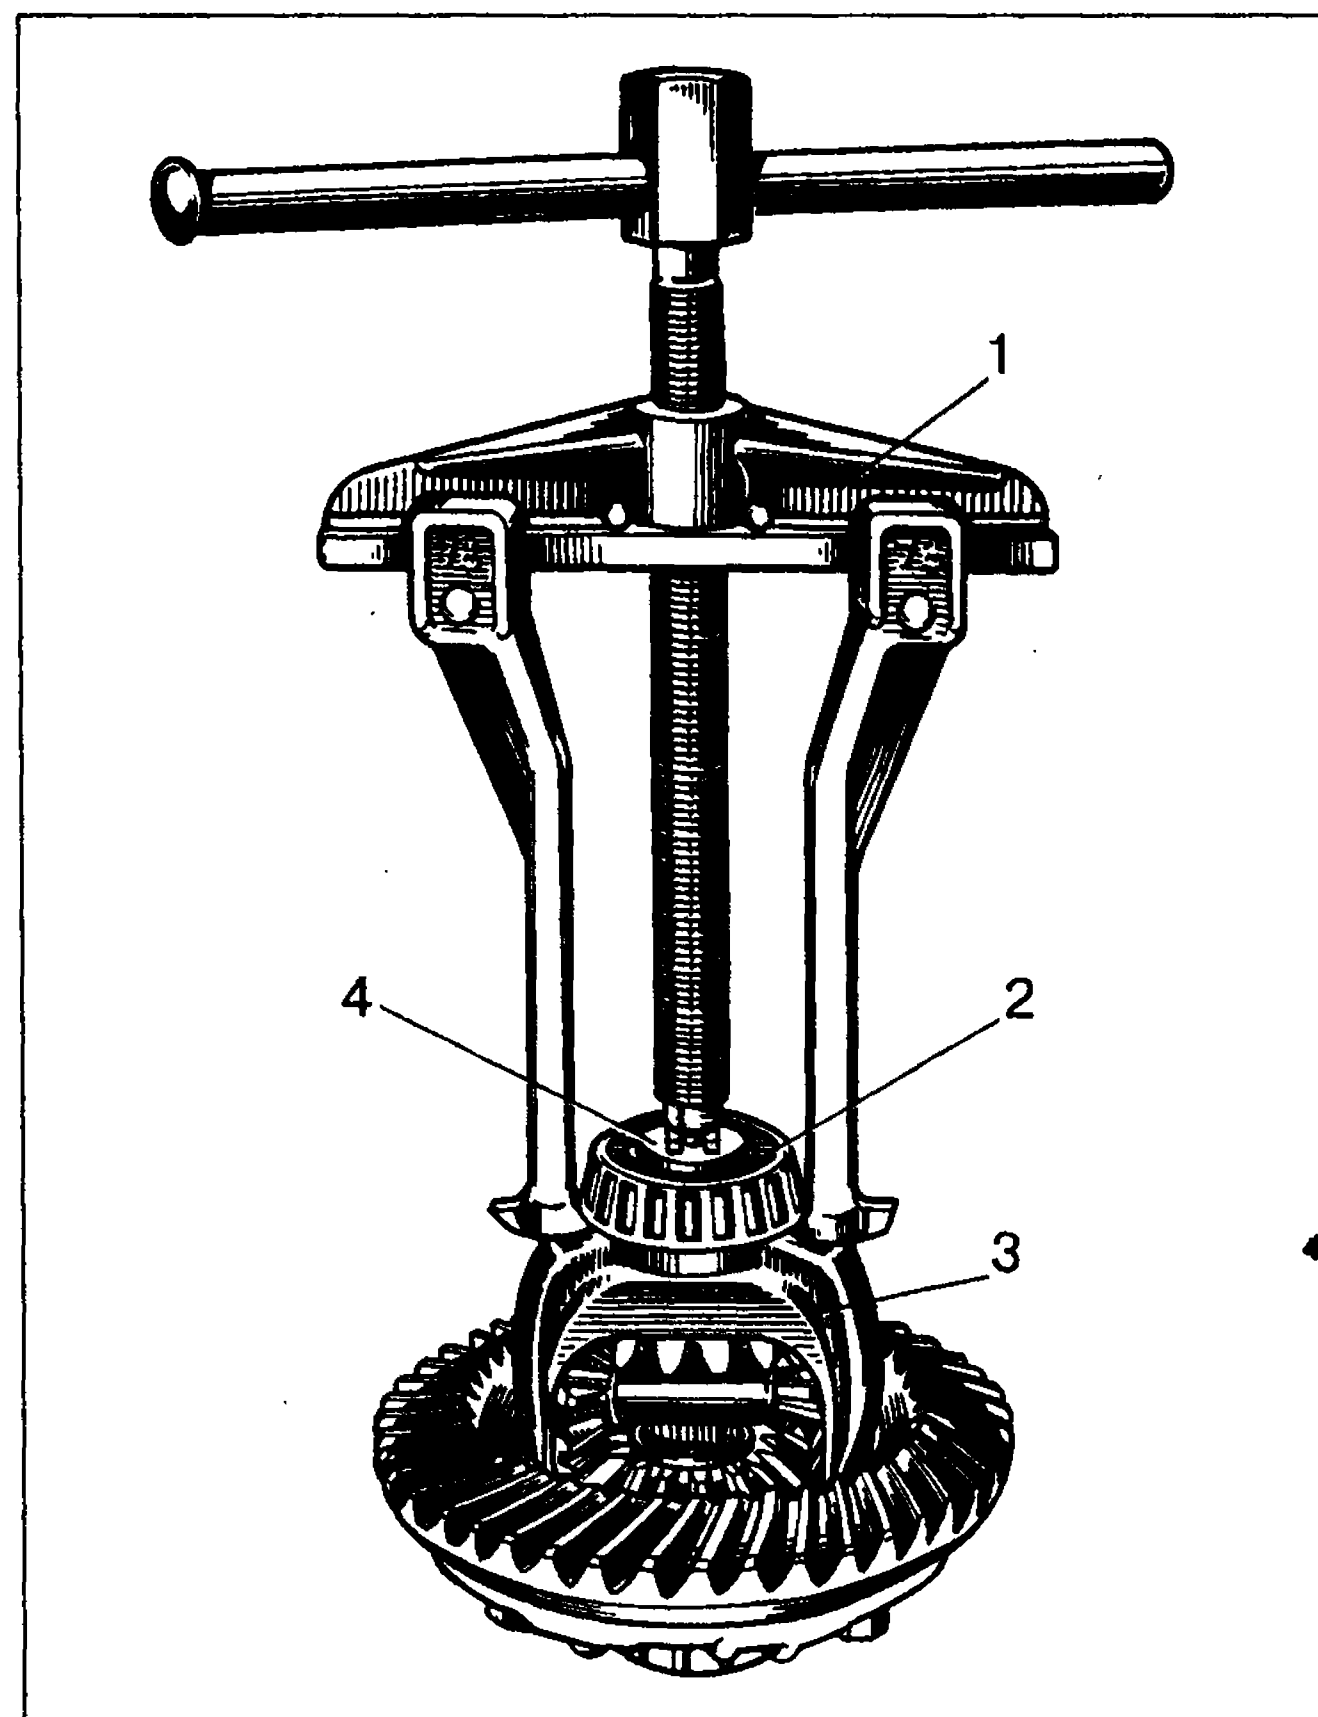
Снятие внутреннего кольца подшипника коробки дифференциала универсальным съемником А.40005/1/6: 1-универсальный съемник А.40005/1/6; 2-внутреннее кольцо подшипника; 3-коробка дифференциала; 4-упор А.45028
